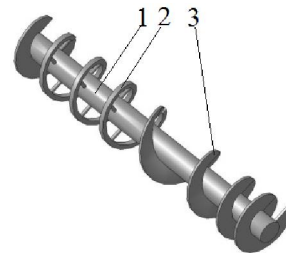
Конструкція комбінованого робочого органу: 1-вал, 2-стрічкова навивка, 3-шнекова навивка
